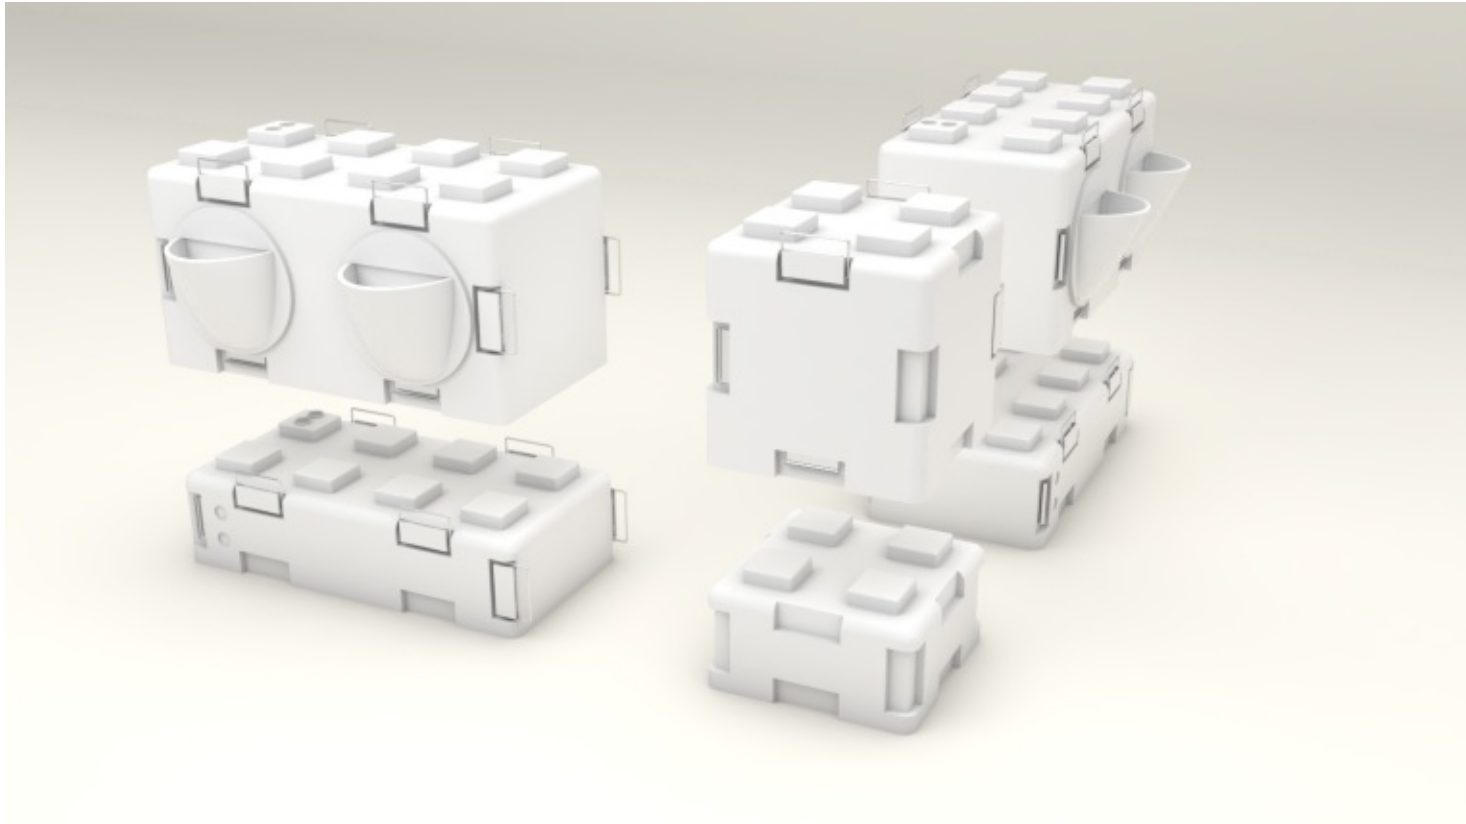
Explosionsdarstellung einer Eckausführung mittels der Verbindermodule (Bildmitte)
